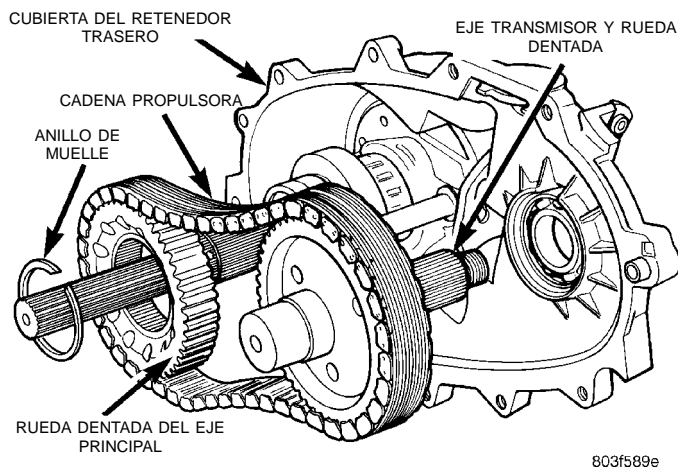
Desmontaje del eje transmisor delantero, el engranaje propulsor y la cadena
